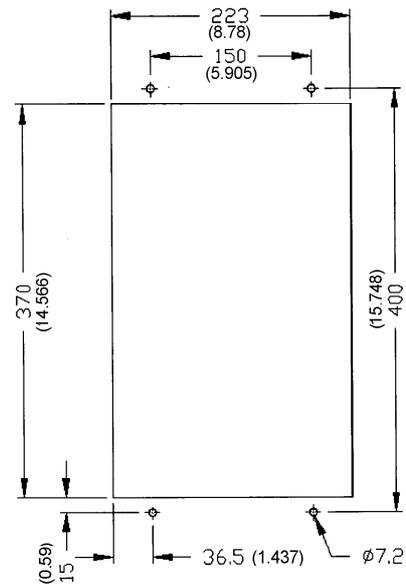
Dimensiones de la abertura para montaje en ducto
